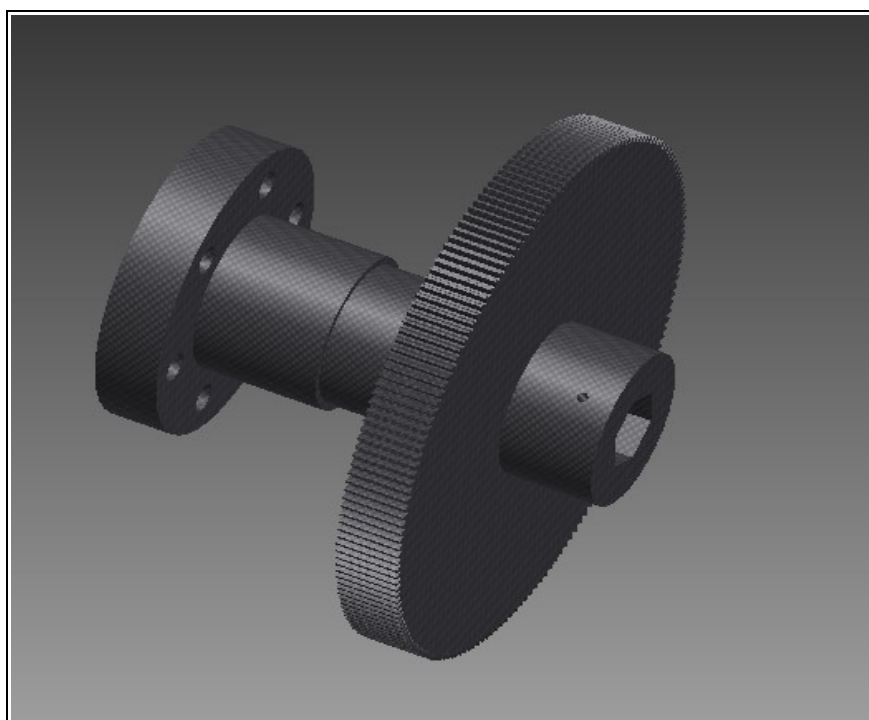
Cigüeñal engranajes, pieza
